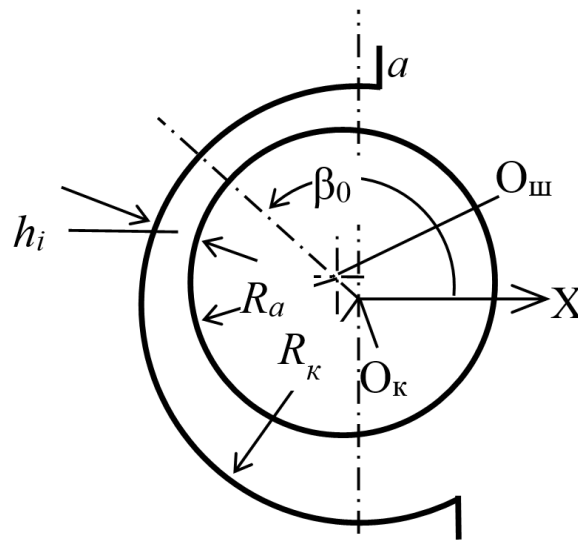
Определение величины зазора h между расточкой корпуса и окружностью выступов зубьев шестерни
